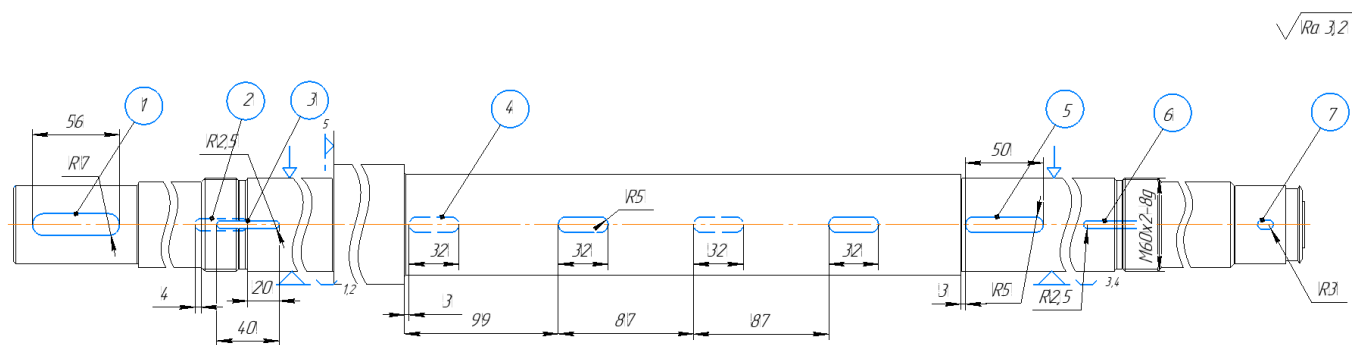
Схема базування заготовки на фрезерній операції 040
